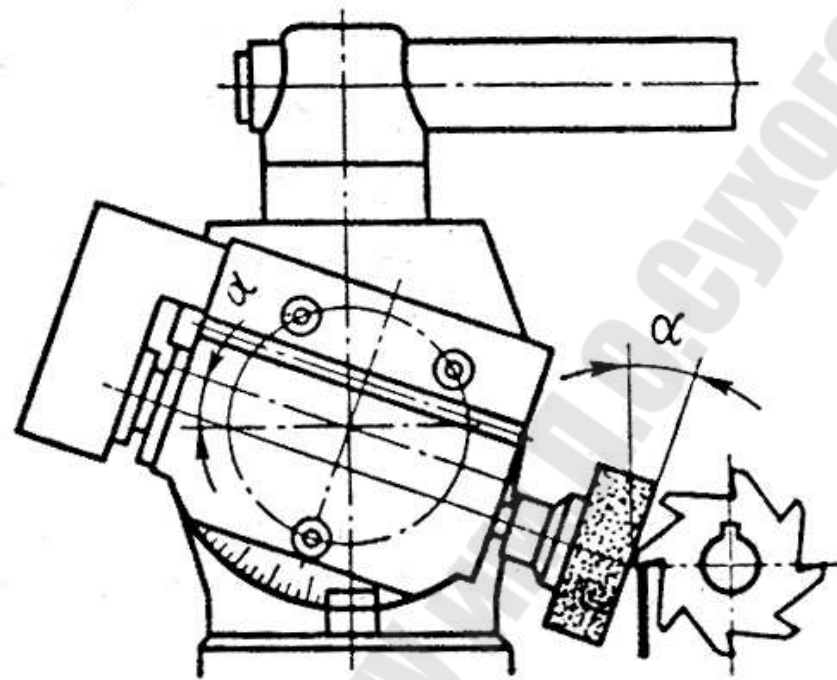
Эскиз шлифовальной бабки станка 3М642
